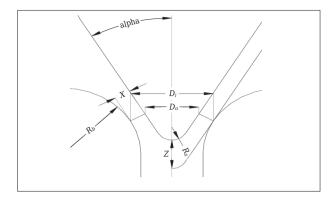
Схема обозначения размеров стопорной пары (стопор-моноблок и стакан-дозатор)
